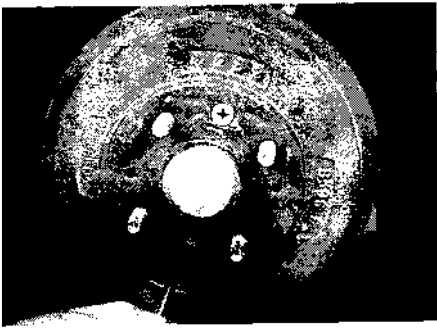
,в. Отверните винты крепления тормозного барабана
